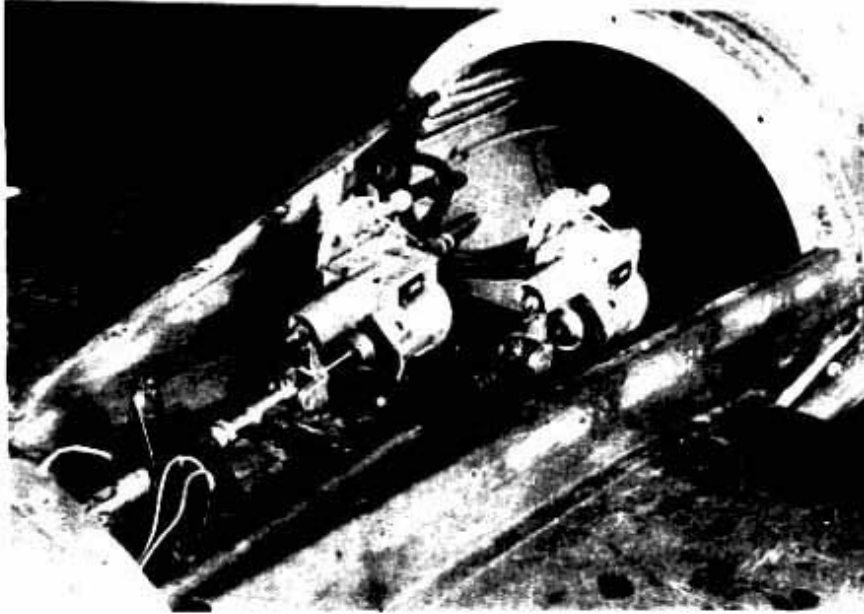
Eingebaute Rudermaschinen im Rumpfheck
